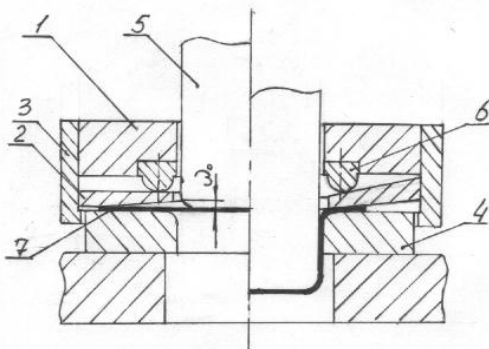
Схема конструкции штампа для вытяжки тонколистового материала с использованием упругого прижима. 1-кольцо опорное; 2-прижим упругий; 3-обойма; 4-матрица; 5-пуансон; 6-выступ кольцевой; 7-заготовка.
